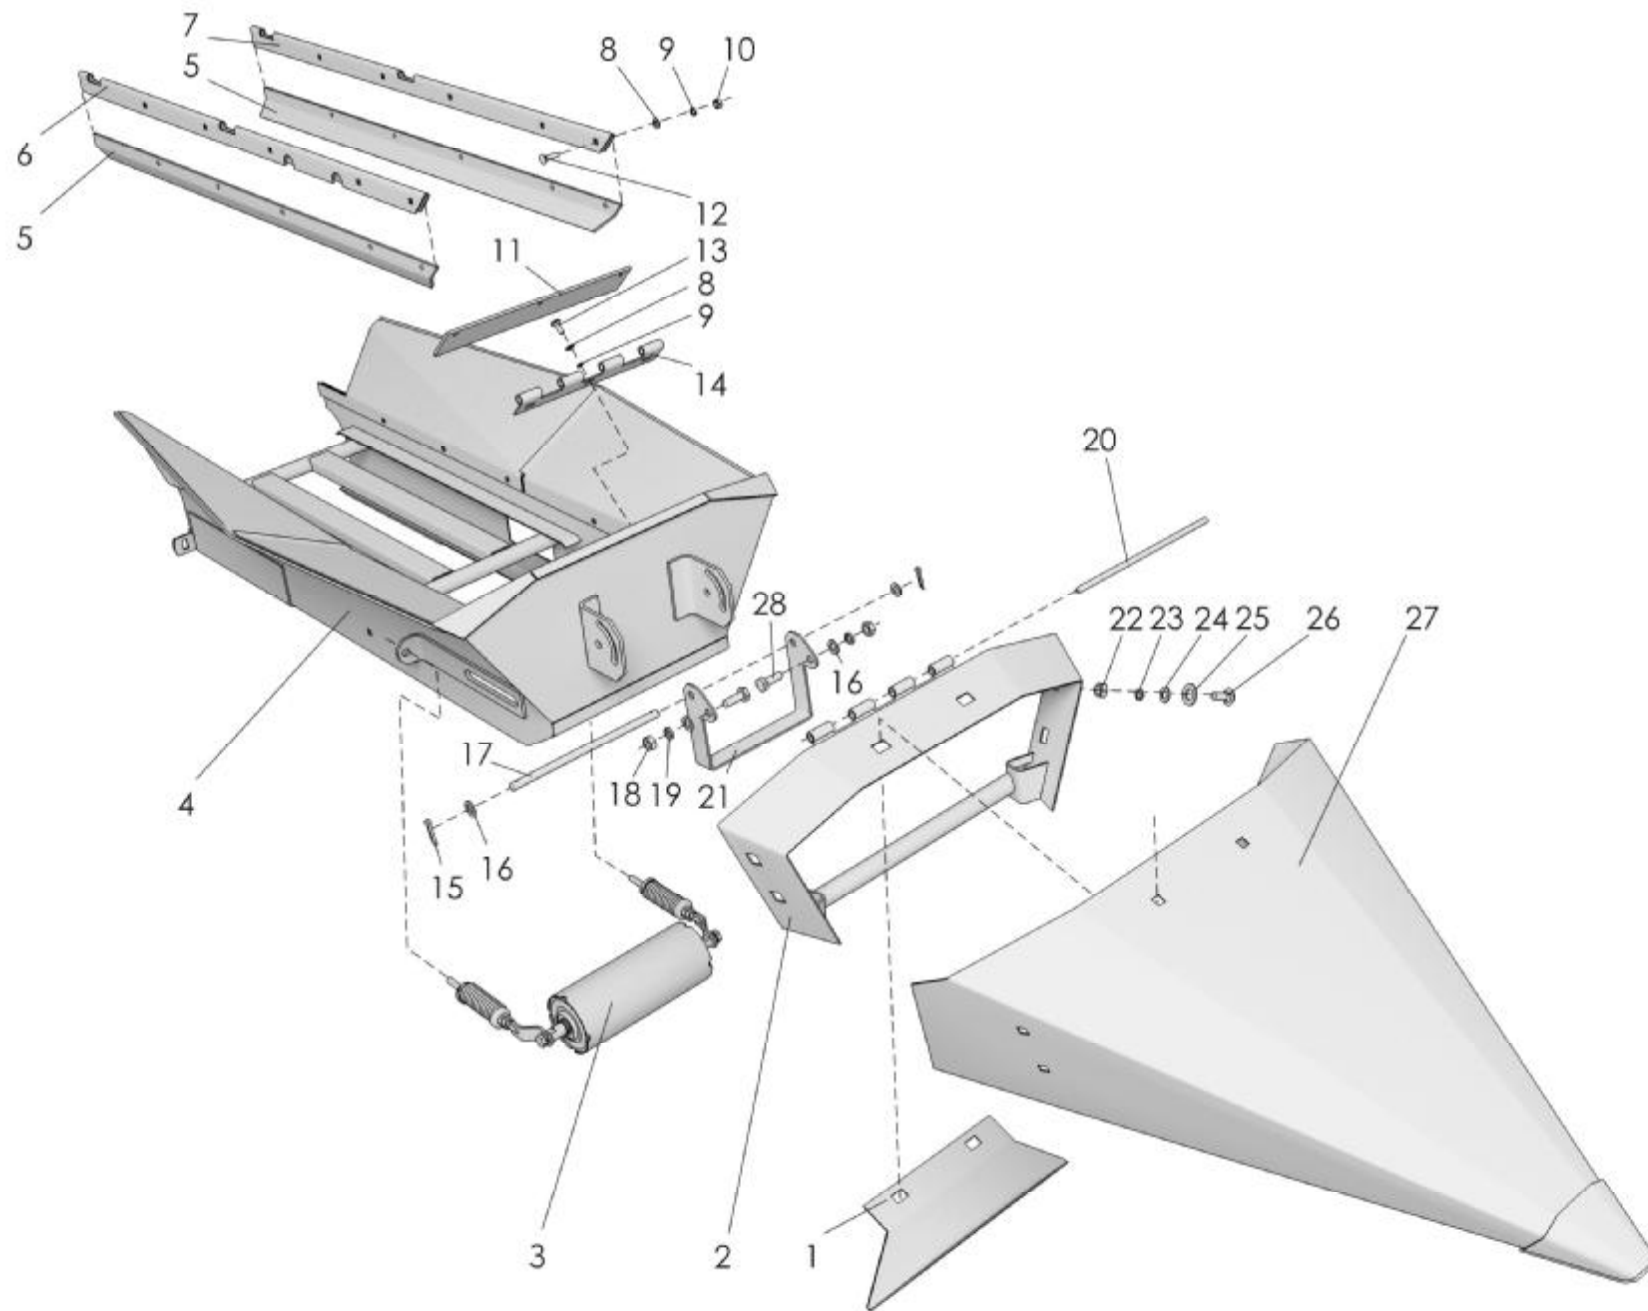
Лифтер центральный ПСП-10М.01.04.000А
